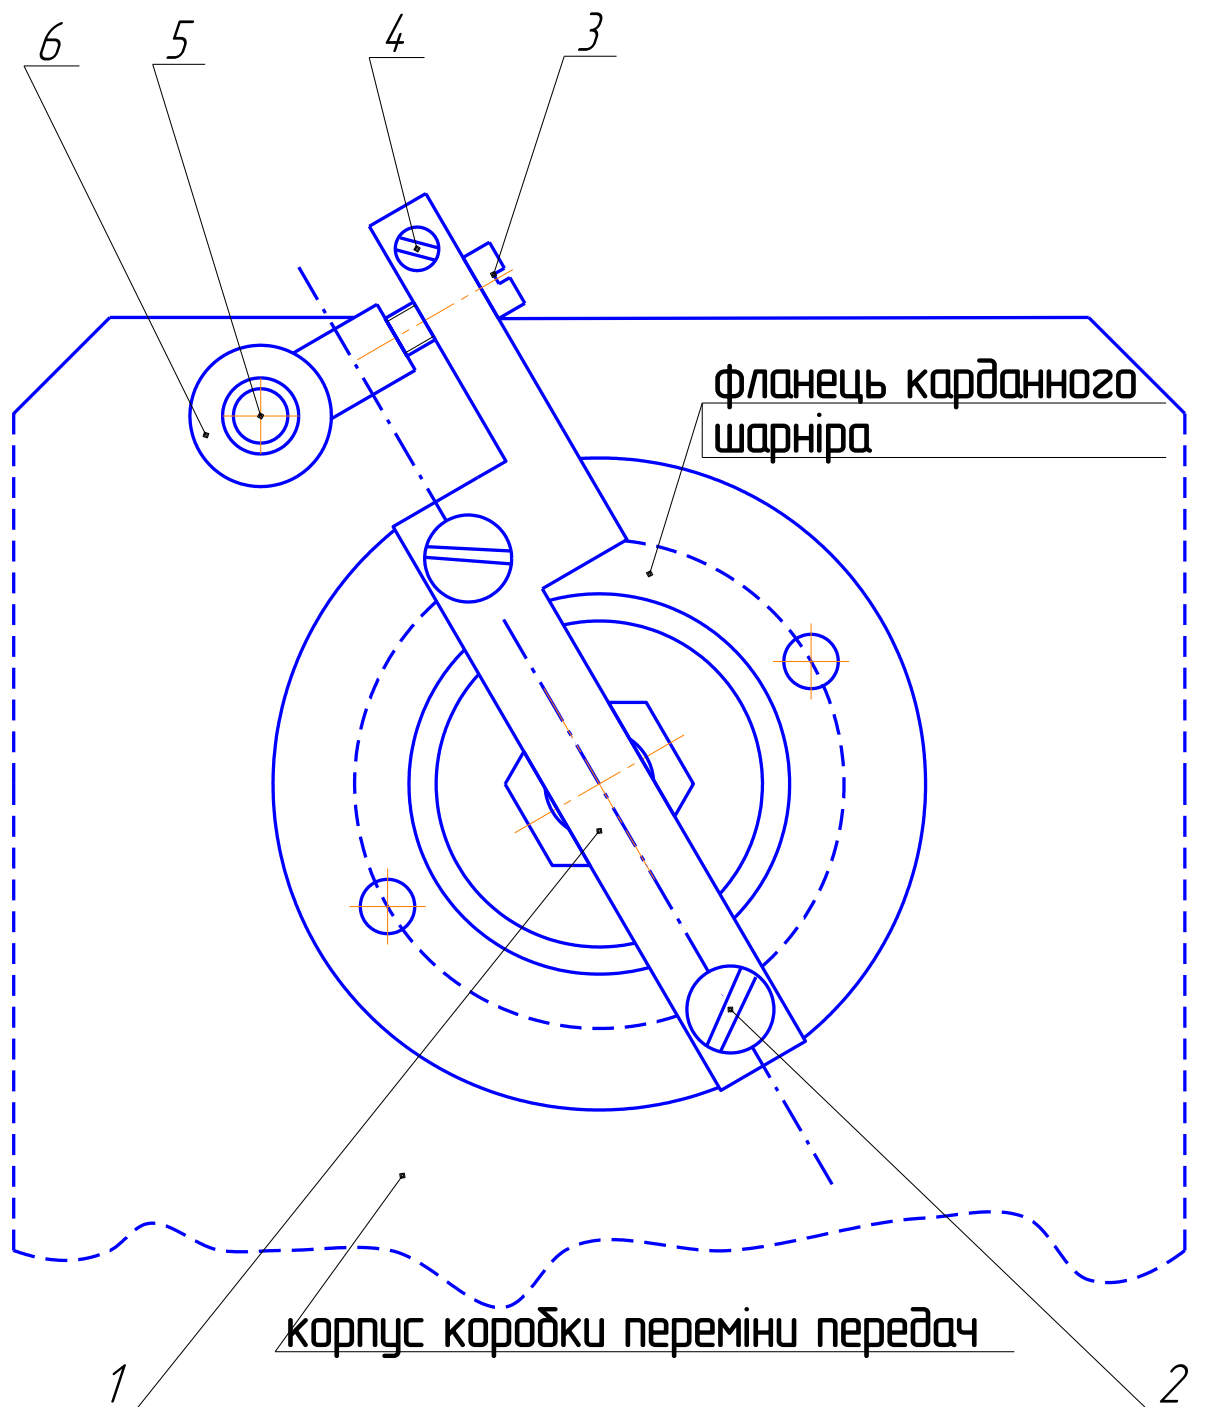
Схема фіксування від обертання вторинного вала коробки передач:
